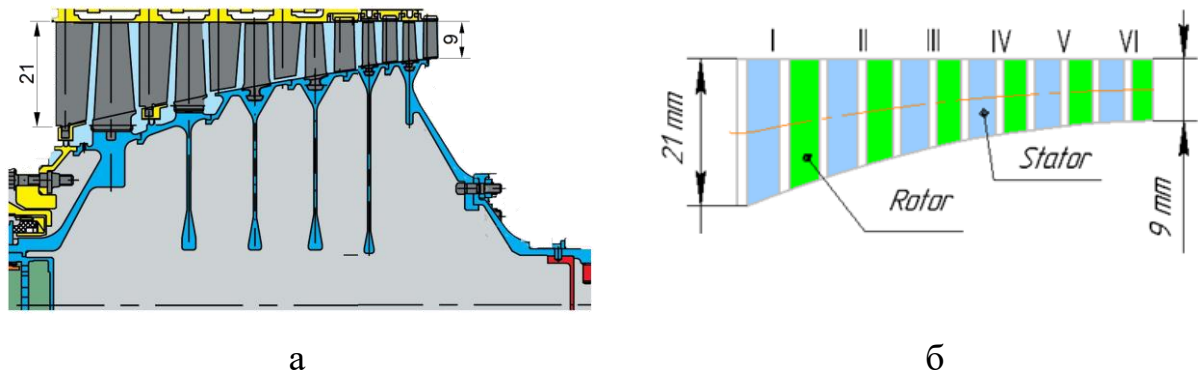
Проточна частина компресора ГТД (а), лопатки ротора і статора (б)
